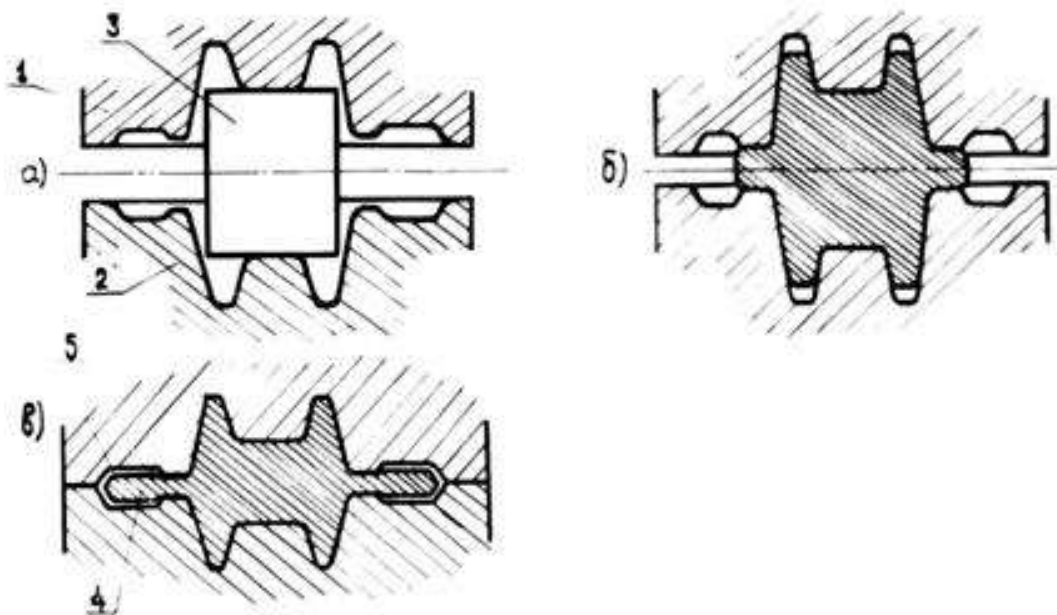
Схема облойного штампування у відкритому штампі: 1,2 – частини штампі; 3 – заготовка; 4 - задирок (облий); 5 - канавка для облою.
